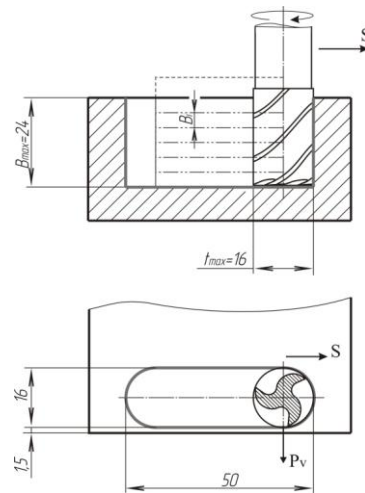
Схема фрезерования паза с тонкой стенкой.
